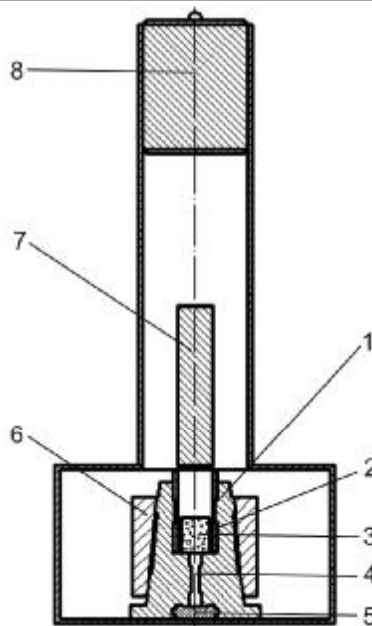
Схема установки для дослідження способу тиксолиття доевтектичного силуміну АК7ч: 1 – прес-форма; 2 – камера пресування; 3 – твердо-рідка заготовка; 4 – порожнина прес-форми; 5 – вставка; 6 – кільце для фіксації прес-форми; 7 – прес-плунжер; 8 – вантаж.
